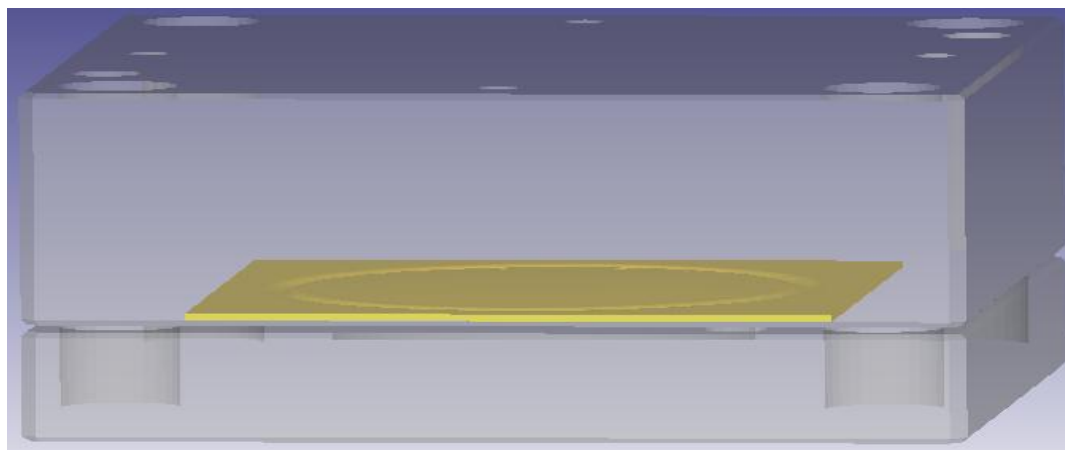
Herramental después del proceso de sujeción para el blanco de 82x82.
